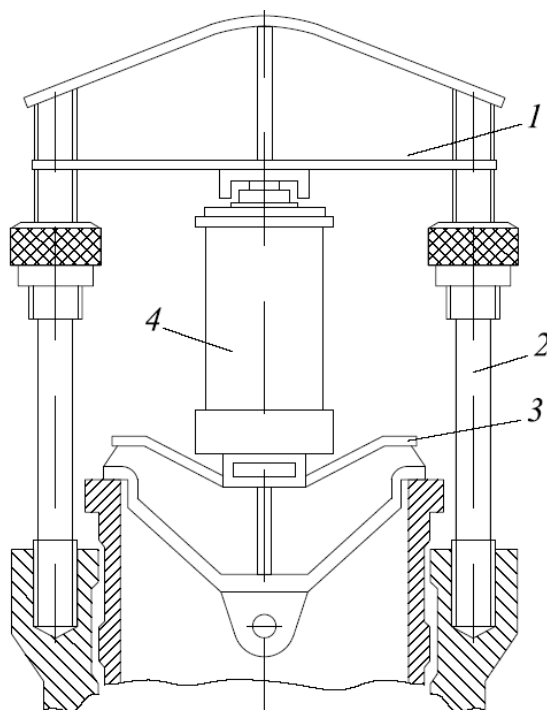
Пристрій для запресовування циліндрових втулок
